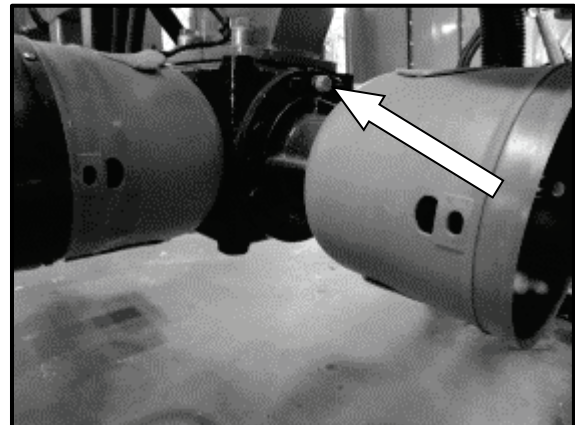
Tornillo de llenado de aceite en el engranaje angular
